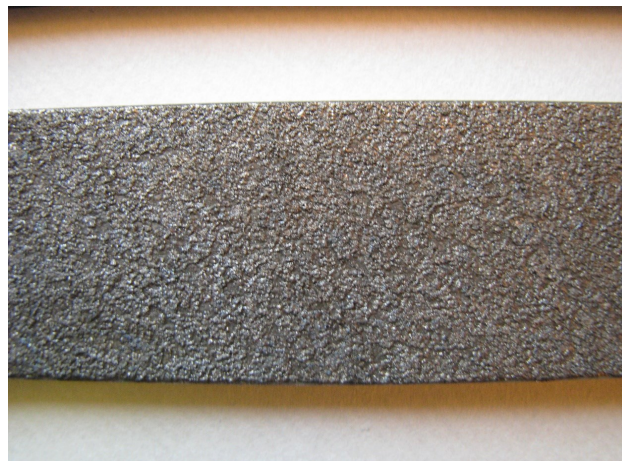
Внешний вид поверхности образця, упрочненного сталью 15X11МФ-III
